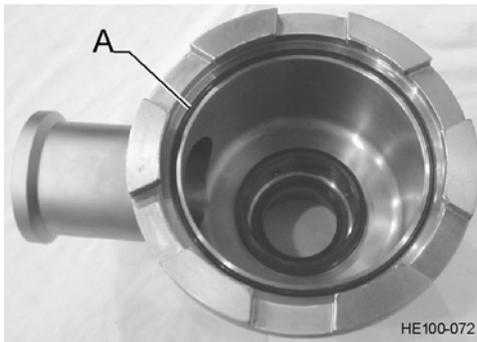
Junta tórica de la cabeza del extremo impulsor opuesto
